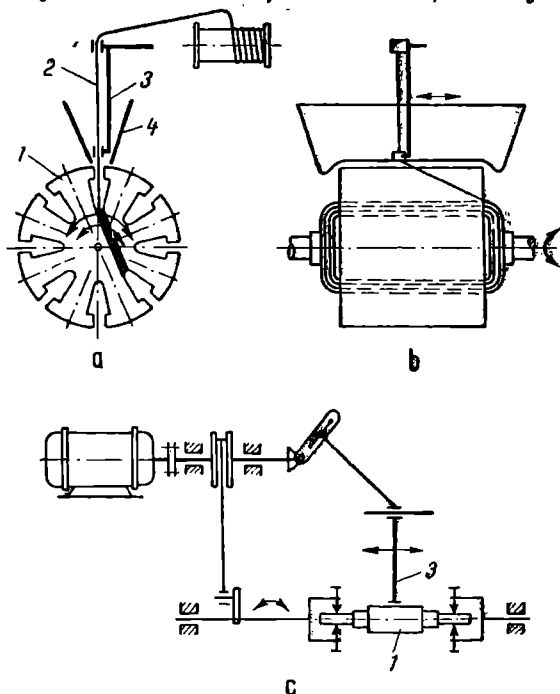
Principiul de funcționare (a, b) și schema cinematică (c) a mașinii automate de bobinat rotoarele motoarelor de putere mică, cu suveică și cu mișcare alternată a indusului :
